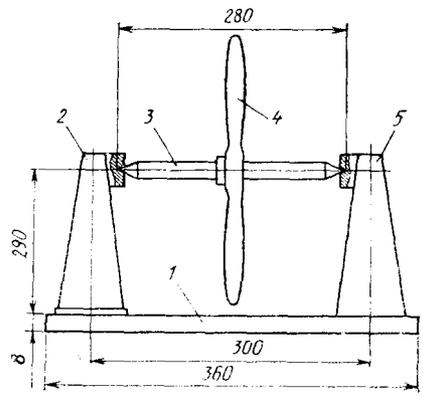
Приспособление для проверки биения и балансировки винта Ш7603-110 ветряка аэропыла:
